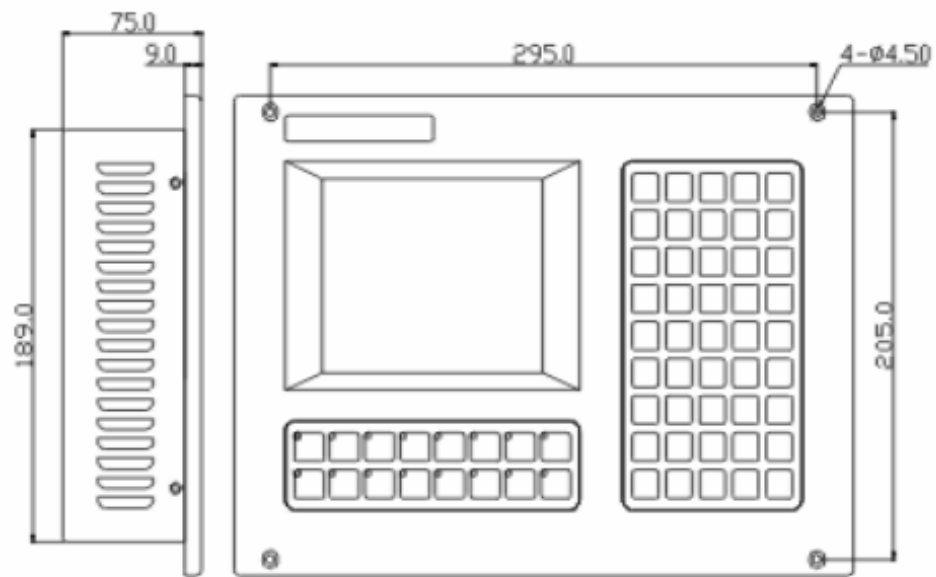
Dimensiones generales del controlador ADTECH CNC 4620
